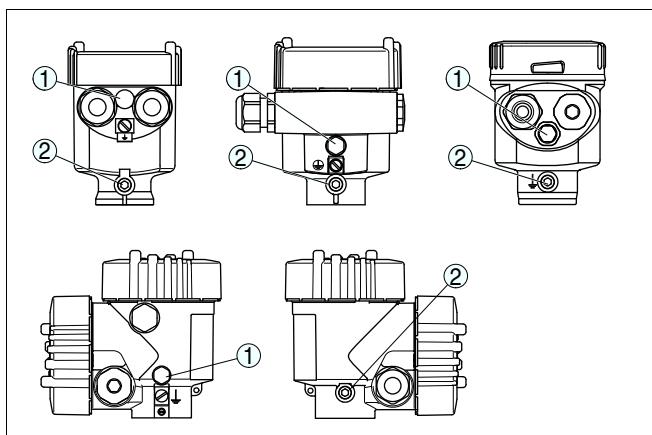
Положение фильтрующего элемента в однокамерном и двухкамерном корпусе
